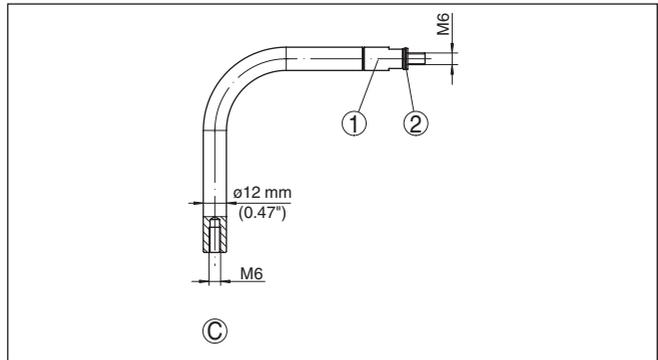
Componentes de varilla con \varnothing 12 mm (0.47 in) - Segmento de arco
